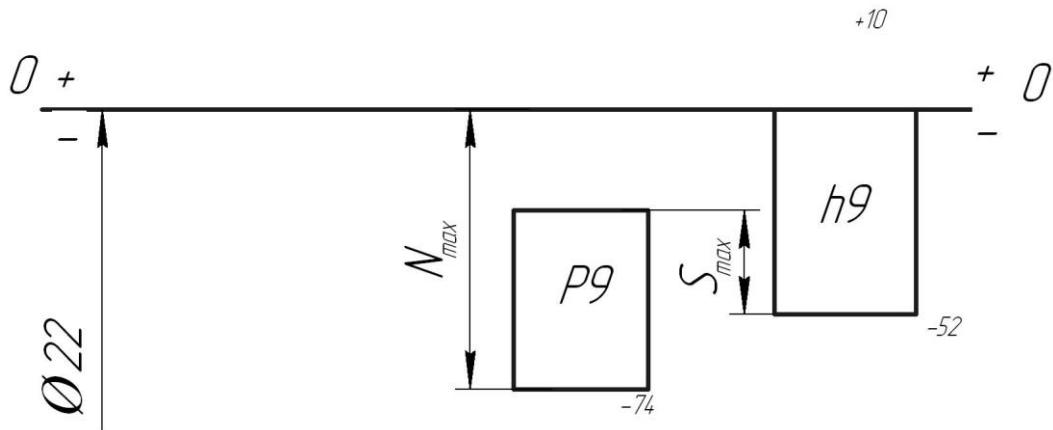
Схема полей допусков соединения шпонка-паз вала
